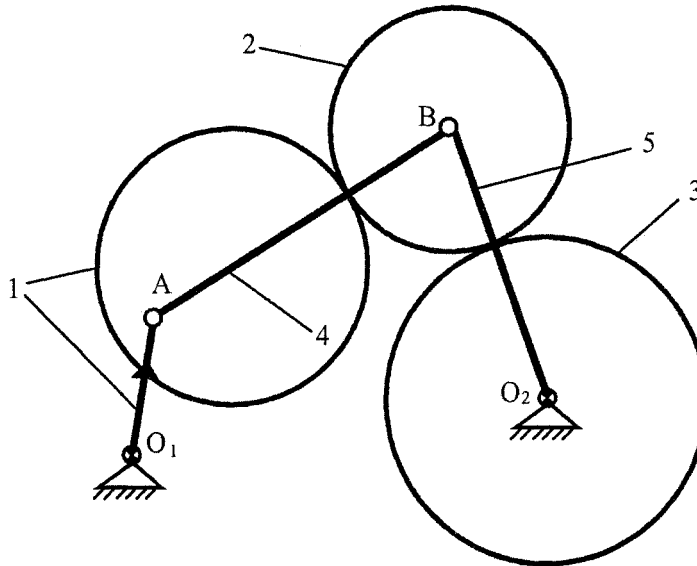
Схема трехколесного зубчато-рычажного механизма периодического движения с круглыми зубчатыми колесами
